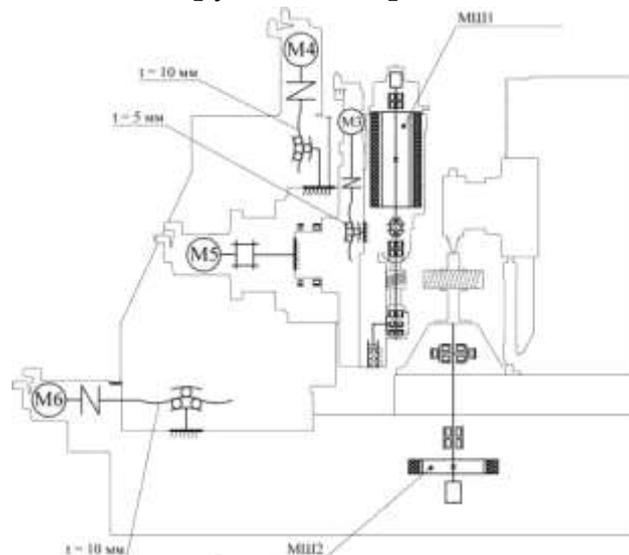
Кинематическая схема вертикального зубофрезерного станка мод. 5320Ф4 с диаметром обработки 200 мм
